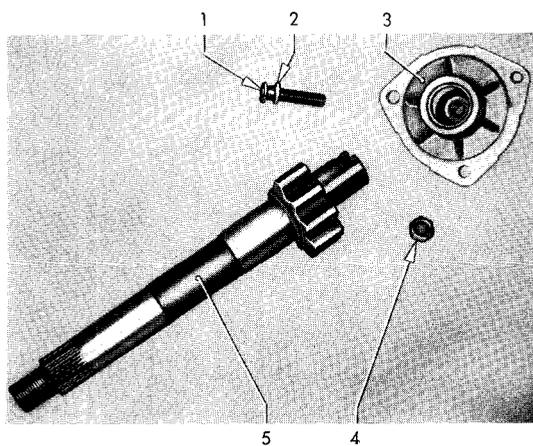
Einstellschraube aus Lenkgehäusedeckel herausgeschraubt
